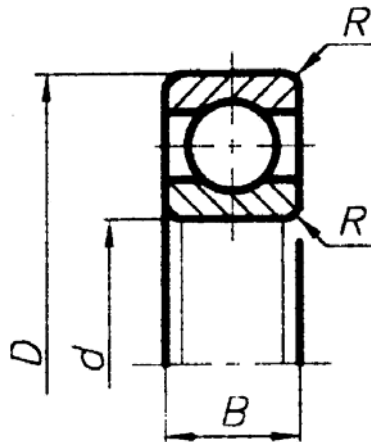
Габаритные размеры шариковых радиальных однорядных подшипников
